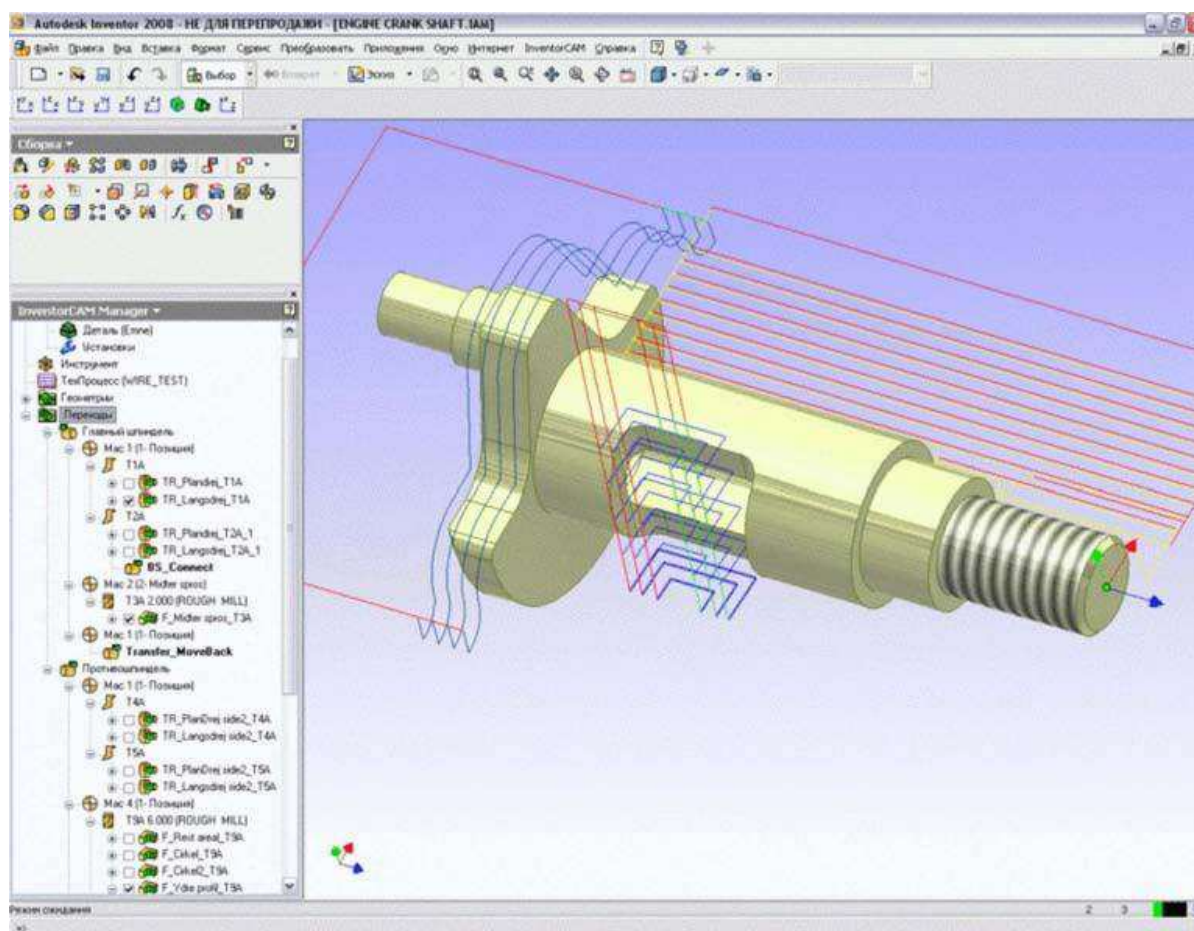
Симуляція токарно-фрезерної обробки
